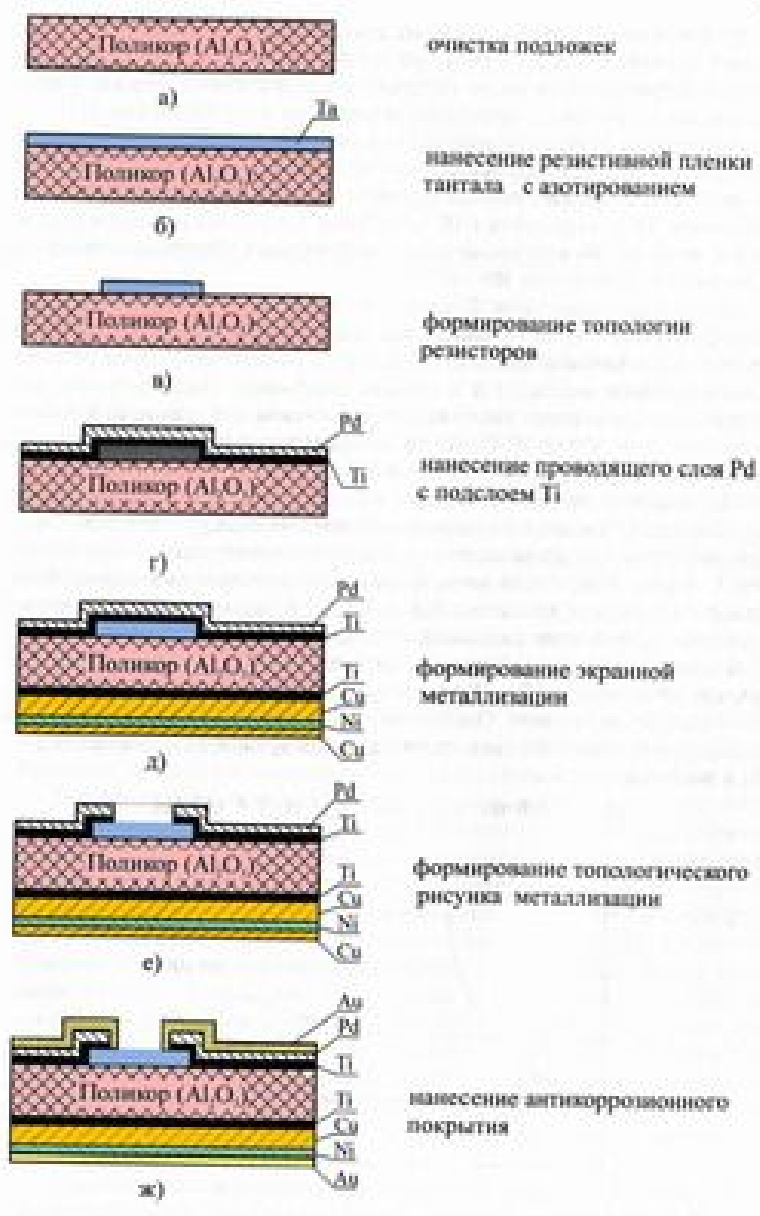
Схема изготовления МПП для бесфлюсовой сборки платы ГИС СВЧ
